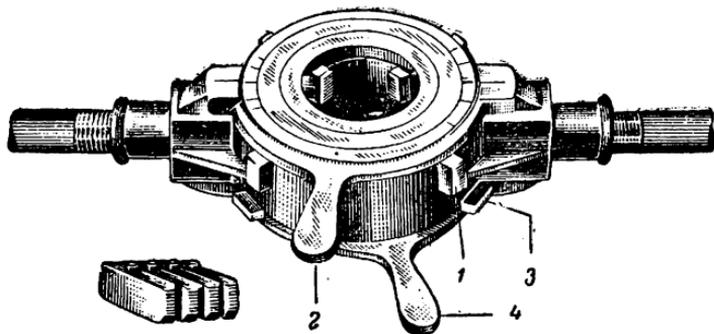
Клупп для нарезания газовой резьбы на трубах: 1—гребенки; 2—верхняя ручка; 3—направляющие; 4—нижняя ручка.
